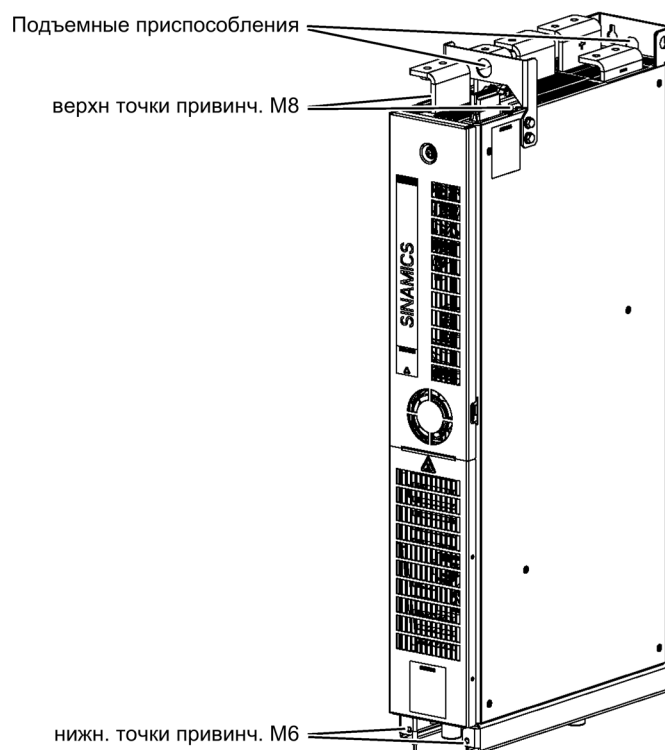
Подъемные приспособления / точки привинчивания для механической опоры
